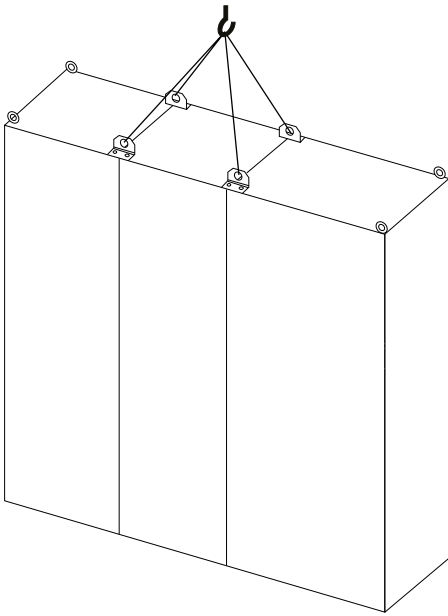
Рекомендуемый способ подъема для корпусов F3/F4/F11/F12/F13
